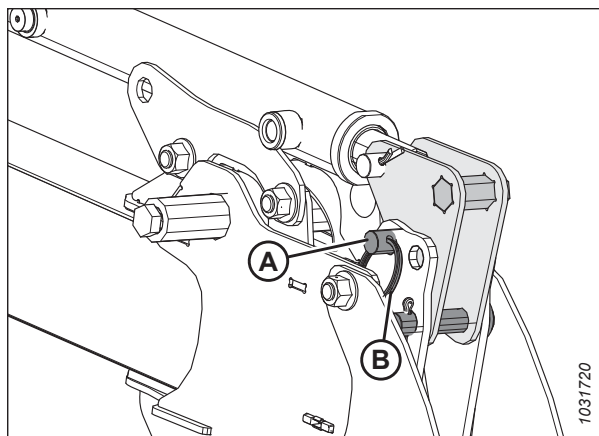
Réglage des vérins avant-arrière de type 1 – Position arrière
